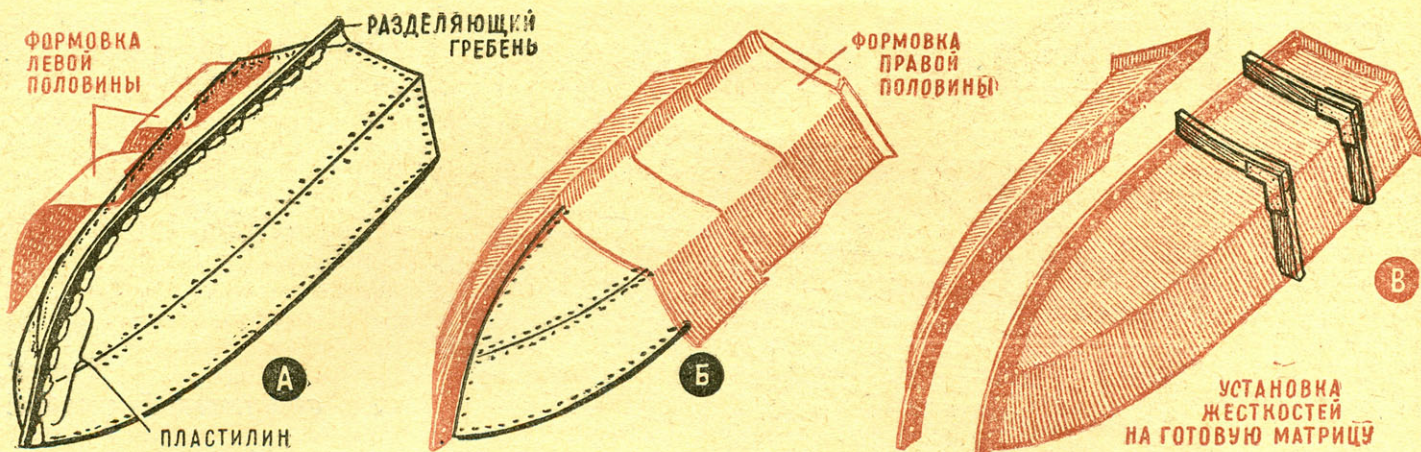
Технология снятия матрицы с готового корпуса мотолодки (или катера): а — установка разделительного гребня из фанеры или жести по киллю с помощью пластилина и формовка левой половины; б — разделительный гребень снят; формовка правой половины выполняется с использованием в качестве упора фланца левой половины; в — установка ребер жесткости на отформованные половинки матрицы. После сборки ребра приформовываются к поверхности матрицы полосками стеклоткани.
